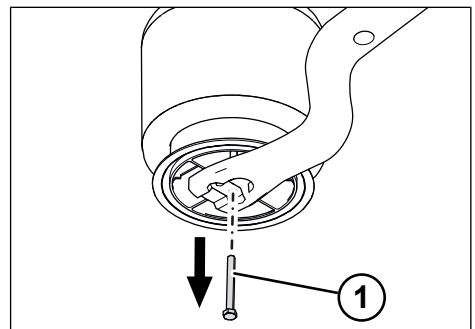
Verschraubung des Luftfederbalgs entfernen
